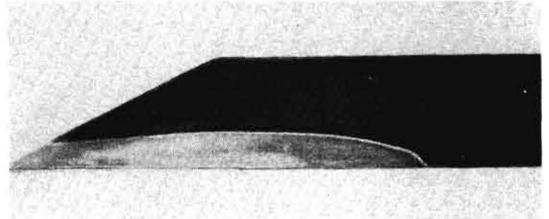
Weiches Häckselmesser mit aufgewalzter Werkzeugstahl-Schneide (Querschliff von Messer VII).
